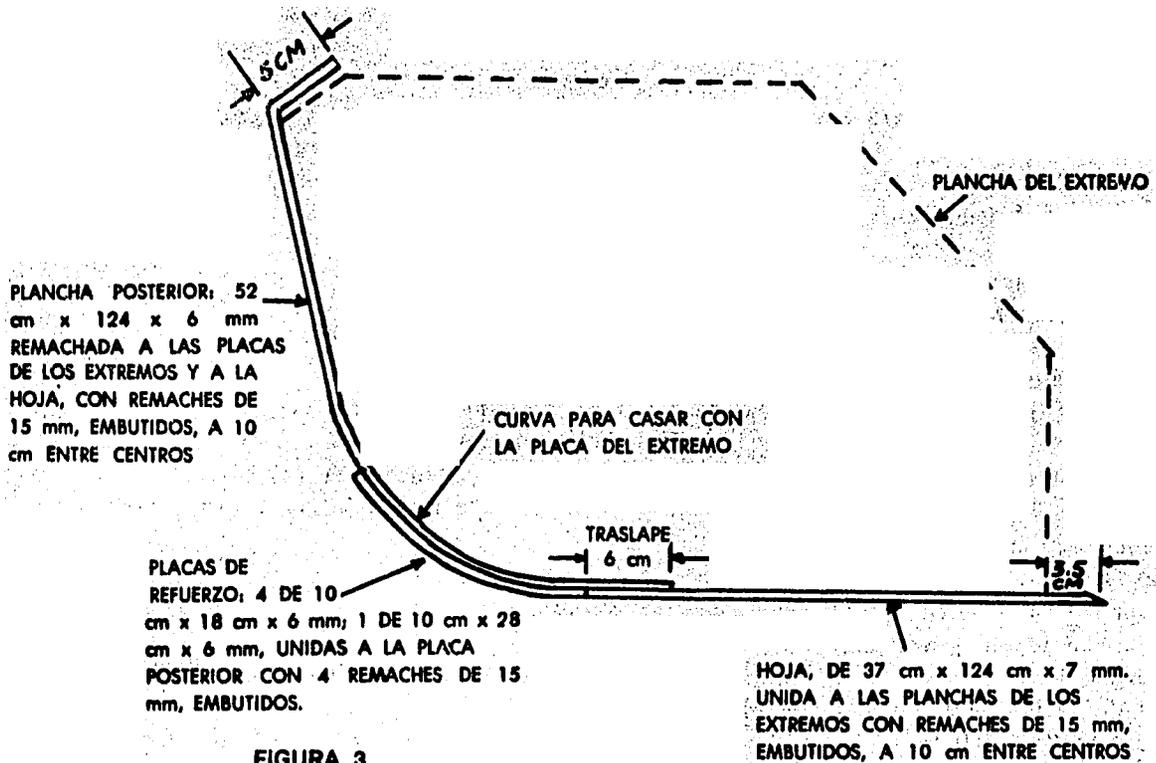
DISPOSICION DE LA HOJA Y DE LAS PLANCHAS POSTERIOR Y DE REFUERZO. VISTA DESDE UN EXTREMO
